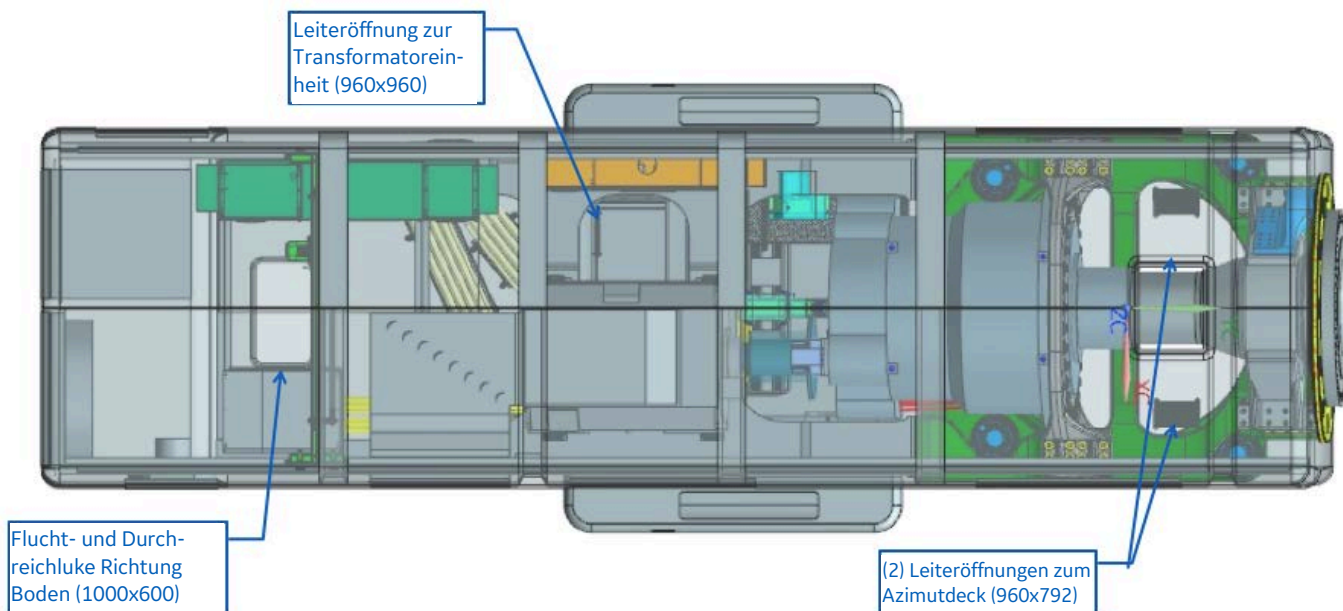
Maschinenhaus Draufsicht: Eintritt- und Austrittswege
